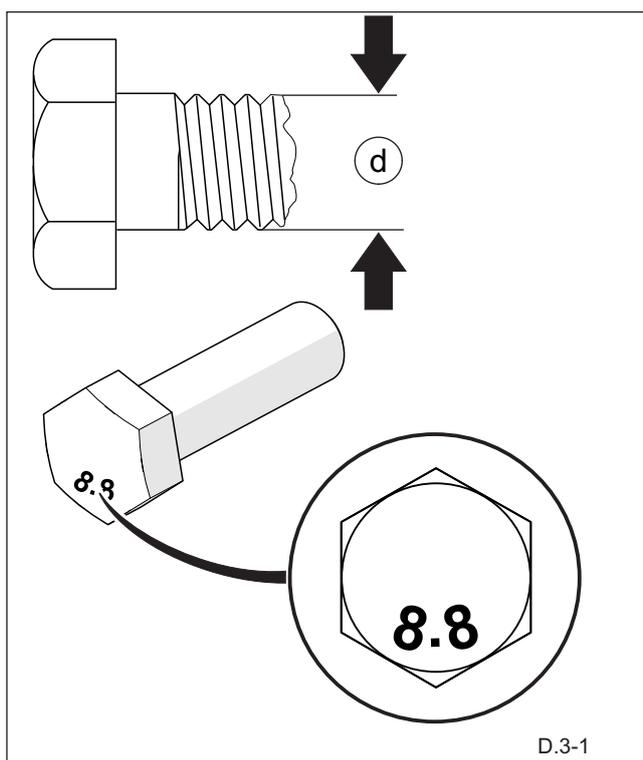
Болт с метрической резьбой (8.8) класс прочности (d) диаметр резьбы
